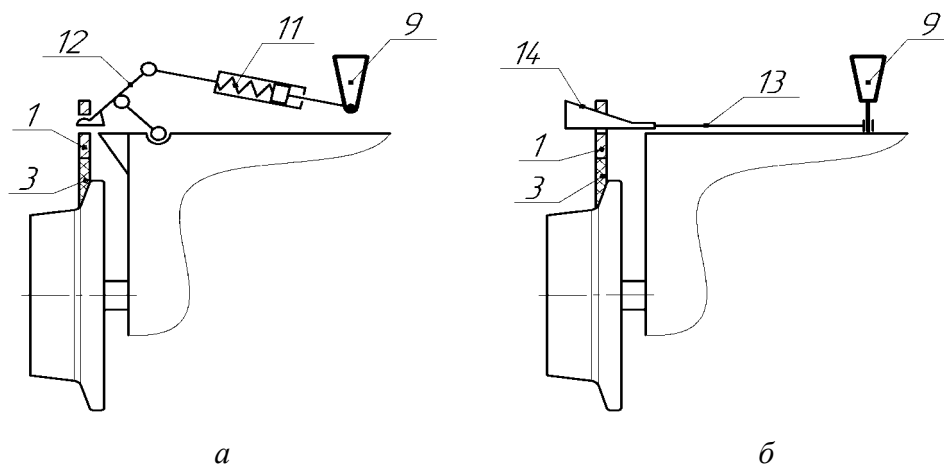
Кінематична схема важільного механізму гребнезмащувача колеса
